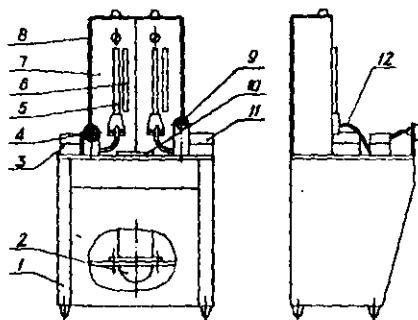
3. Схема пневматического измерительного прибора: 1-корпус; 2-баллон; 3 и 11-стабилизаторы давления; 4 и 9-пневмопробки; 5-стеклянная трубка; 6-шкала; 7-панель; 8-щиток; 10-плита; 12-трубка полихлорвиниловая
